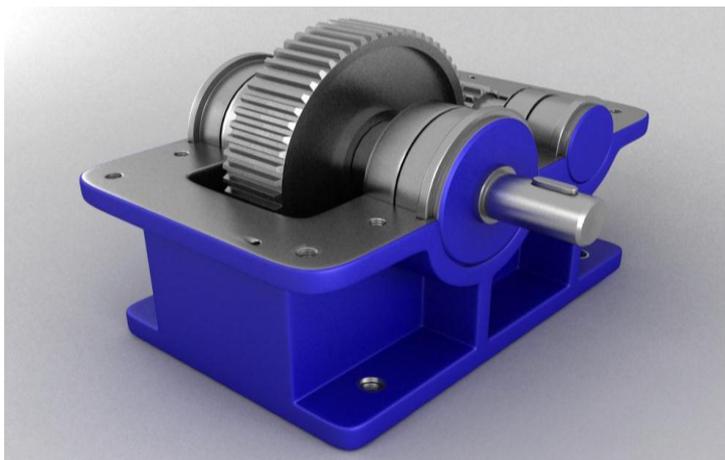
Цилиндрический одноступенчатый редуктор в сборе без крышки.
